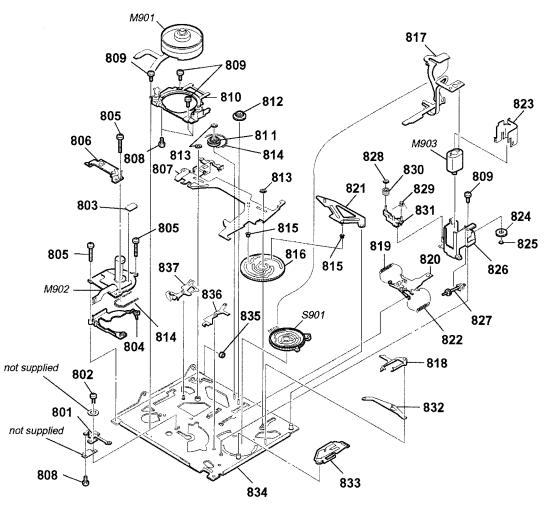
Узлы направляющих стоек, прижимного ролика, ленточного тормоза, переключатель формата, контактор блокиратора записи
